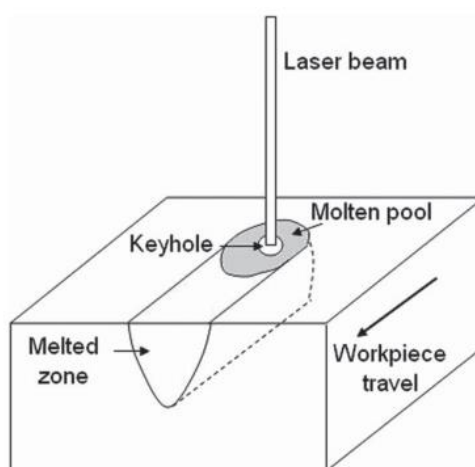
Схема лазерной проникающей сварки [1]
